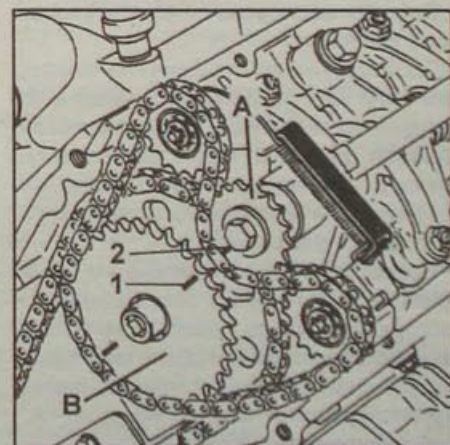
Установка звездочек распределительного и балансировочного валов:
